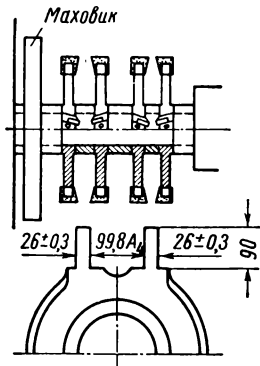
Схема фрезерования двойной проушины набором из четырех твердосплавных дисковых фрез
